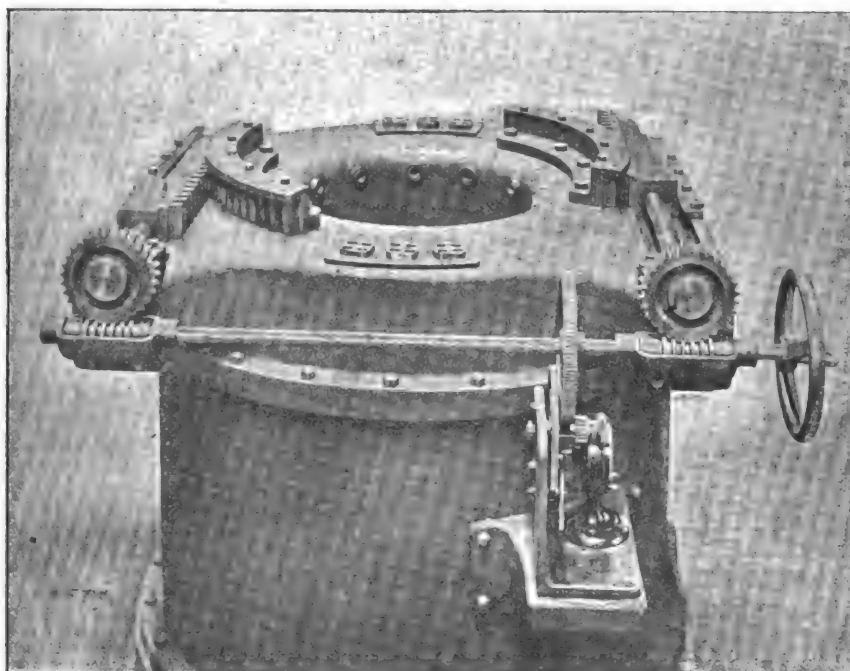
Vue extérieure du régulateur de la Carborundum Company.
